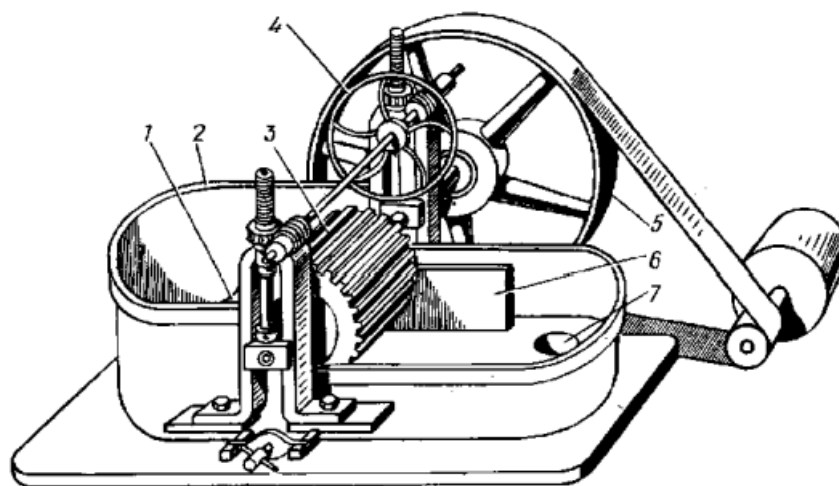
Устройство ролла: 1 – горка с планкой; 2 – металлическая ванна; 3 – размольный барабан; 4 – вылегчивающее устройство; 5 – приводной шкив на валу; 6 – перегородка; 7 – отверстие для слива
